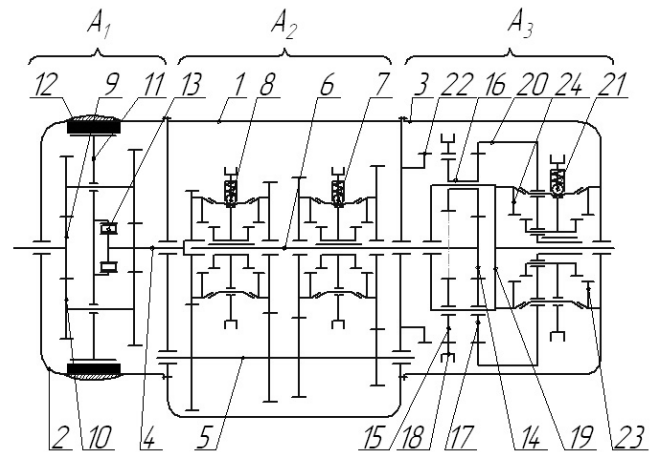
Кинематическая схема многоступенчатой коробки передач: A_1 – дифференциальный делитель; A_2 – основной редуктор; A_3 – дифференциальный демультипликатор; 1 – корпус основного редуктора; 2 – картер сцепления (картер дифференциального делителя); 3 – картер дифференциального демультипликатора; 4 – первичный вал основного редуктора; 5 – промежуточный вал основного редуктора; 6 – вторичный вал основного редуктора; 7 и 8 – синхронизаторы соответственно первой–второй и третьей–четвертой передач основного редуктора; 9 – входной вал-шестерня дифференциального делителя; 10 – двухвенцовые сателлиты дифференциального делителя; 11 – водило дифференциального делителя; 12 – ленточные тормоза; 13 – муфта свободного хода; 14 – ведущий зубчатый венец дифференциального демультипликатора; 15 – сателлиты дифференциального демультипликатора; 16 – двухвенцовые сателлиты дифференциального демультипликатора; 17 – паразитные сателлиты дифференциального демультипликатора; 18 – коронное колесо (муфта заднего хода) дифференциального демультипликатора; 19 – водило дифференциального демультипликатора (выходной вал коробки передач); 20 – коронное колесо дифференциального демультипликатора; 21 – синхронизатор дифференциального демультипликатора; 22 – зубчатый венец блокировки муфты заднего хода; 23 – зубчатый венец блокировки коронного колеса дифференциального демультипликатора; 24 – зубчатый венец блокировки дифференциального демультипликатора
